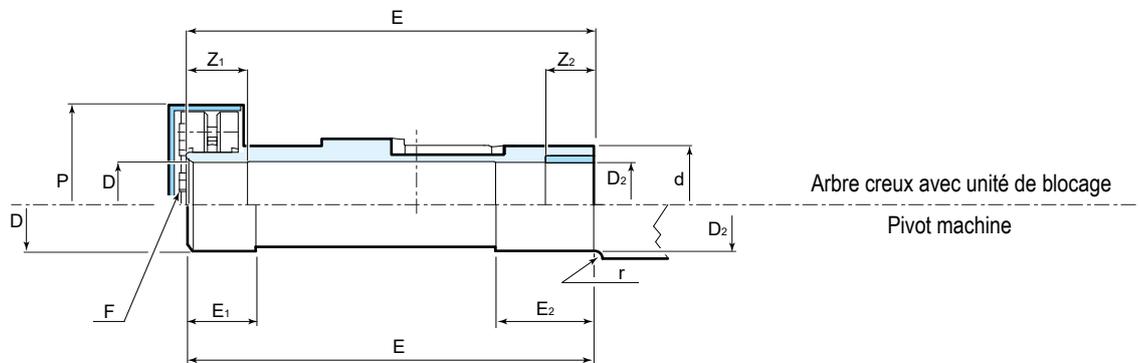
Arbre lent creux et axe de machine avec unité de serrage
